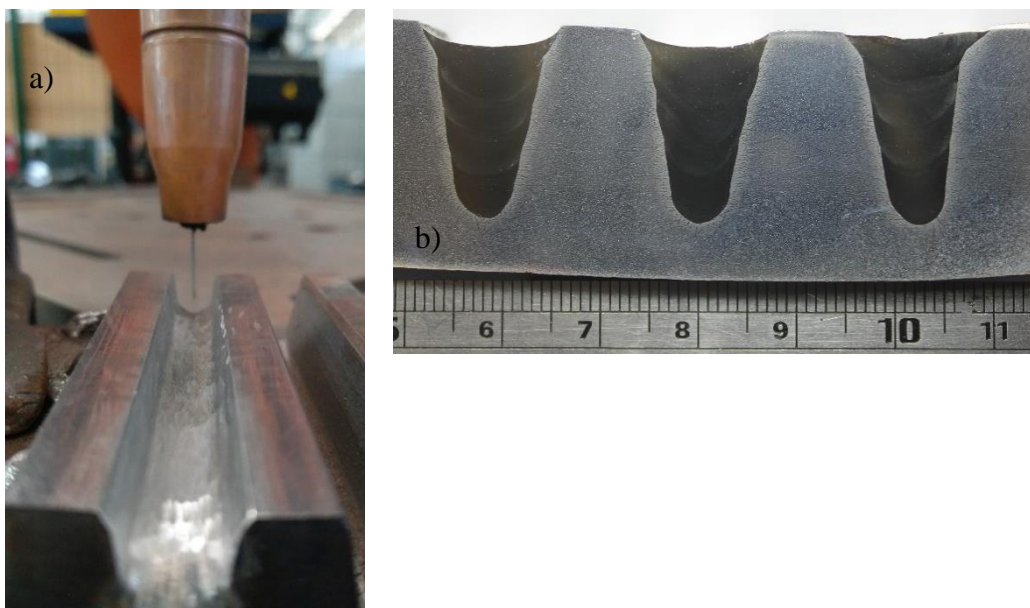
a) Soldagens exploratórias e b) apresentação de cordões com defeitos
